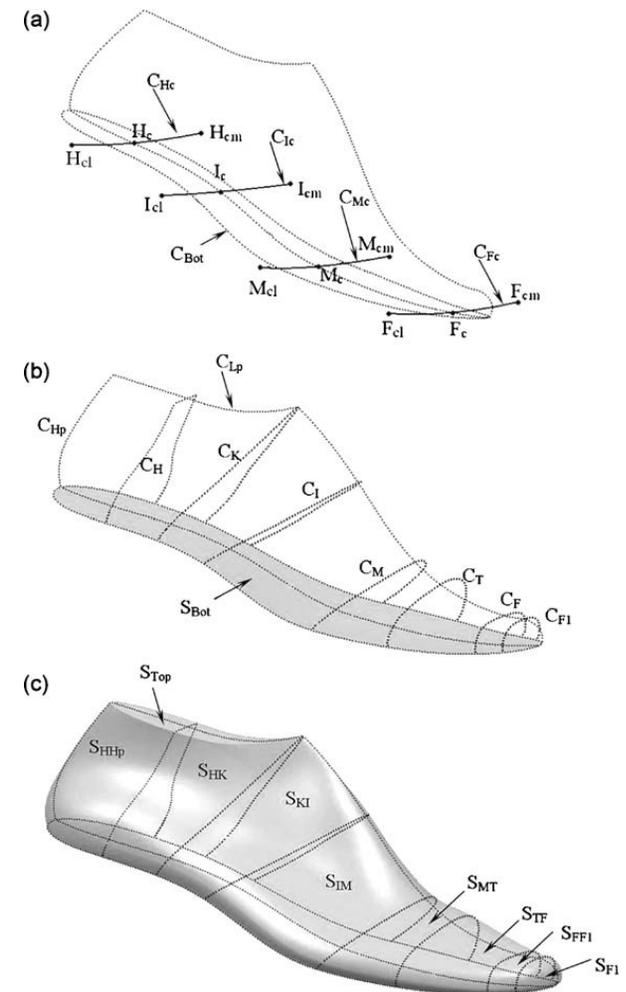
Secciones constructivas de la horma (Luximon & Luximon, 2009)
